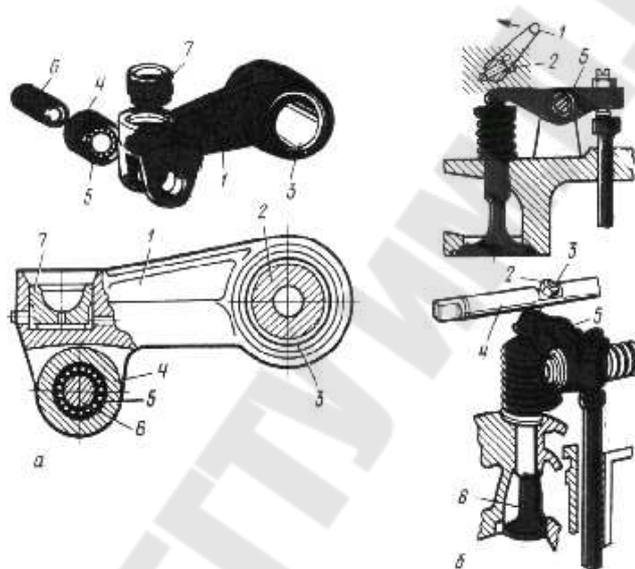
Толкатель и декомпрессионный механизм дизеля А-41
